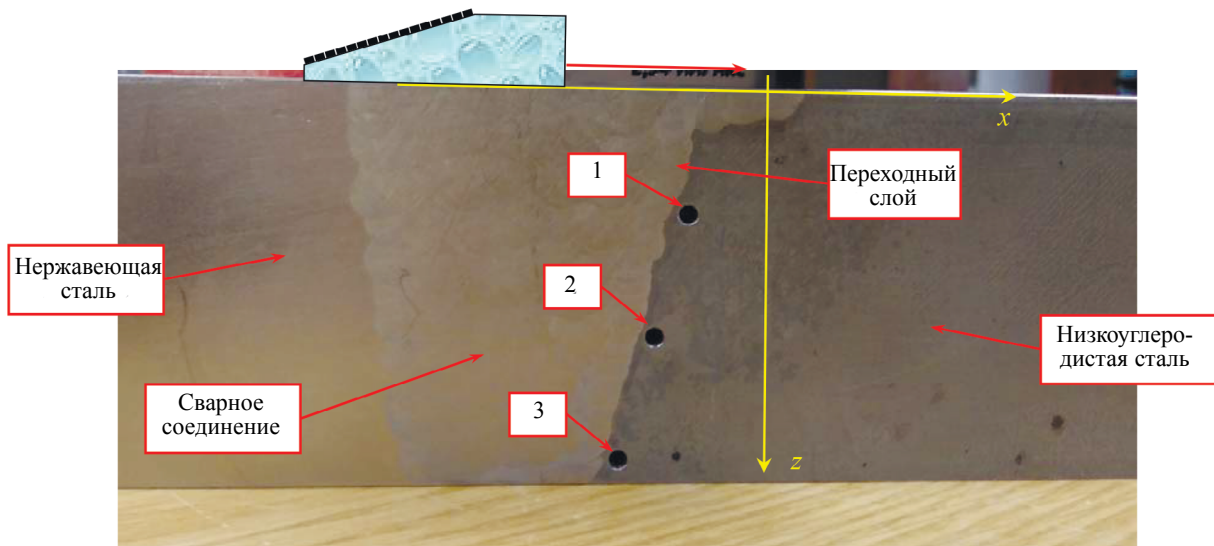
Образец с композитным сварным соединением трубопровода Ду1100.
